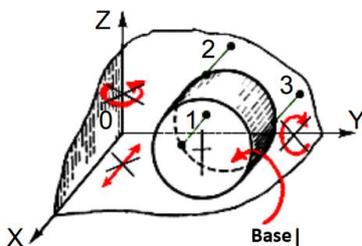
Base de fixation pour les pièces cylindriques courtes
